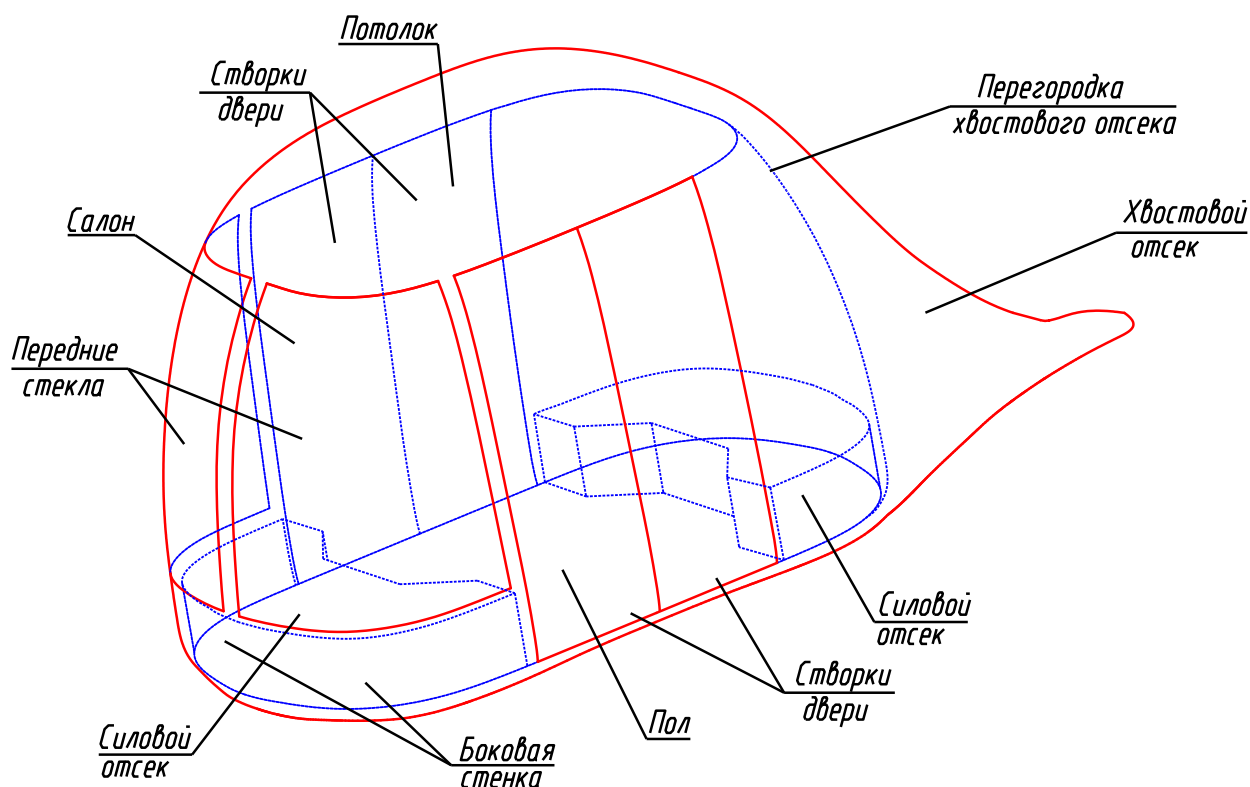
Внешний вид юнибуса Ю-324П-01
